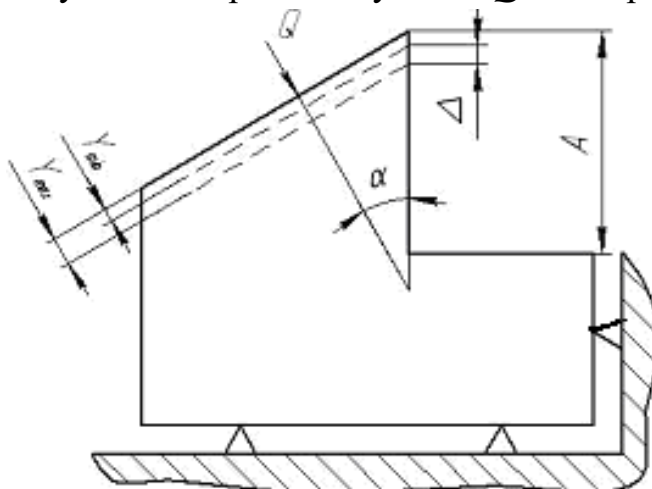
Розрахункова схема для визначення похибки закріплення
